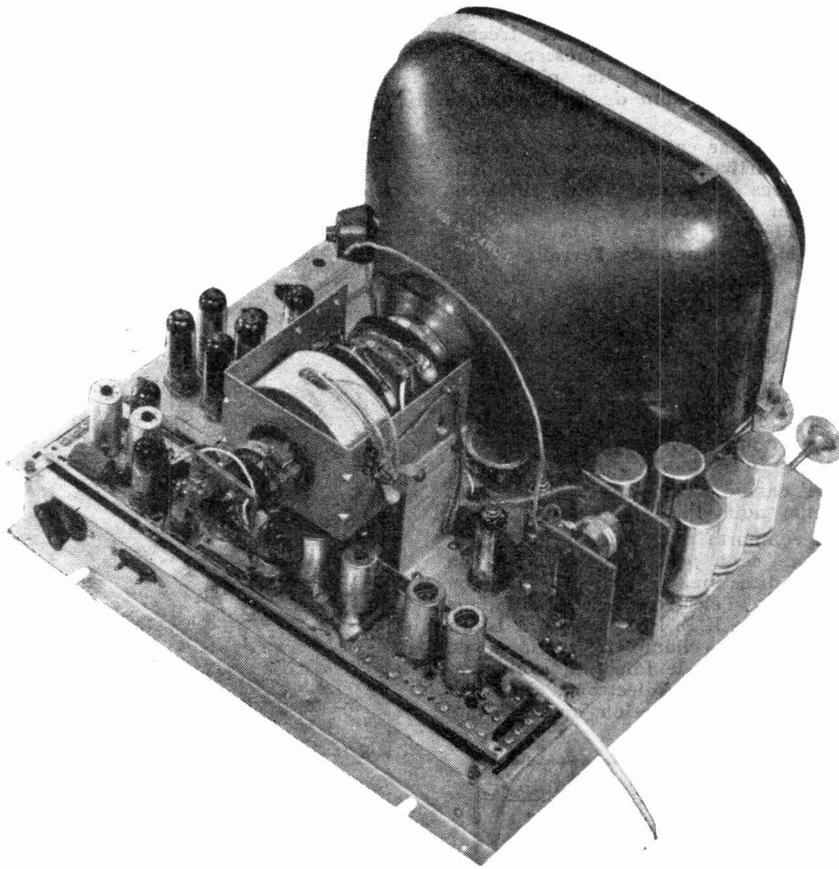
Installation de tous les dispositifs accessoires sur le tube cathodique et montage du tube sur le châssis d'un téléviseur moderne (VIDEON).
